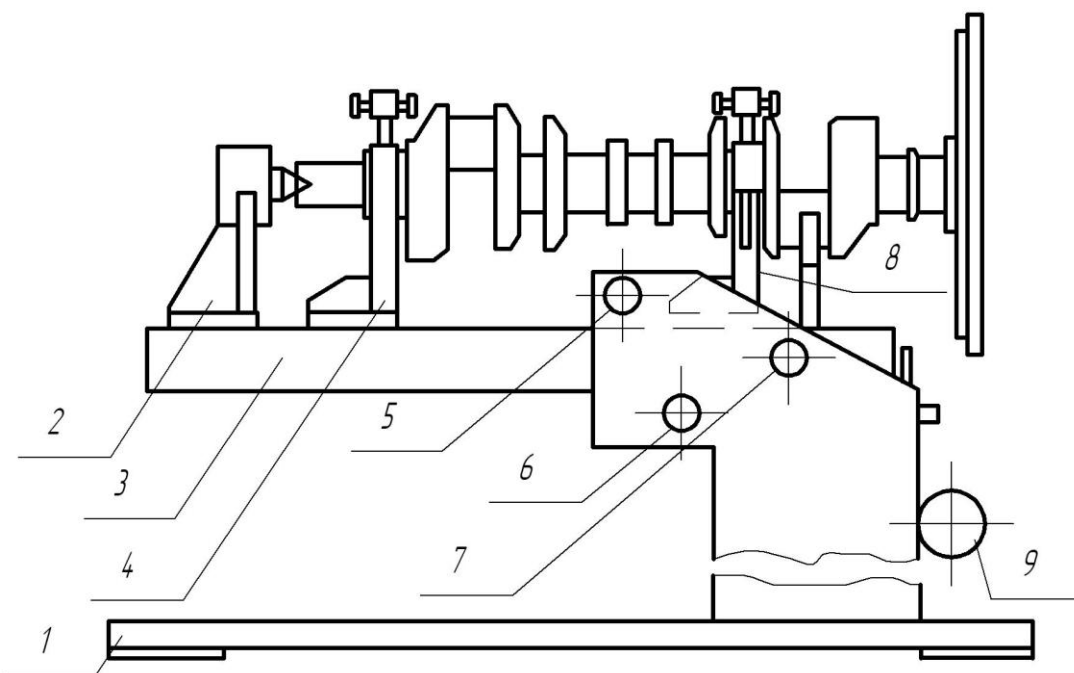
Стенд для разборки и сборки коленчатого вала:
